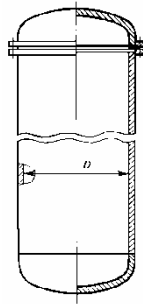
З'єднання еліптичної кришки і днища з корпусом апарата
